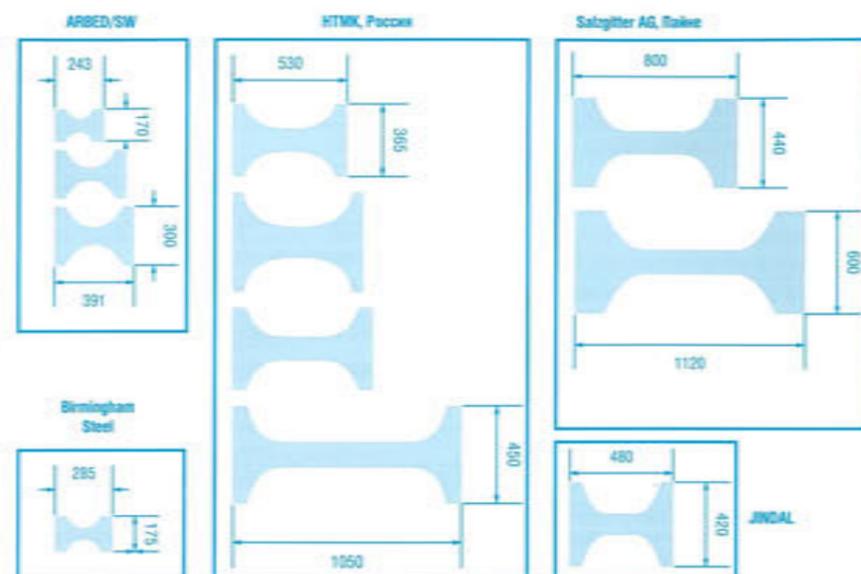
Непрерывнолитые балочные заготовки, получаемые на оборудовании фирмы VIM
